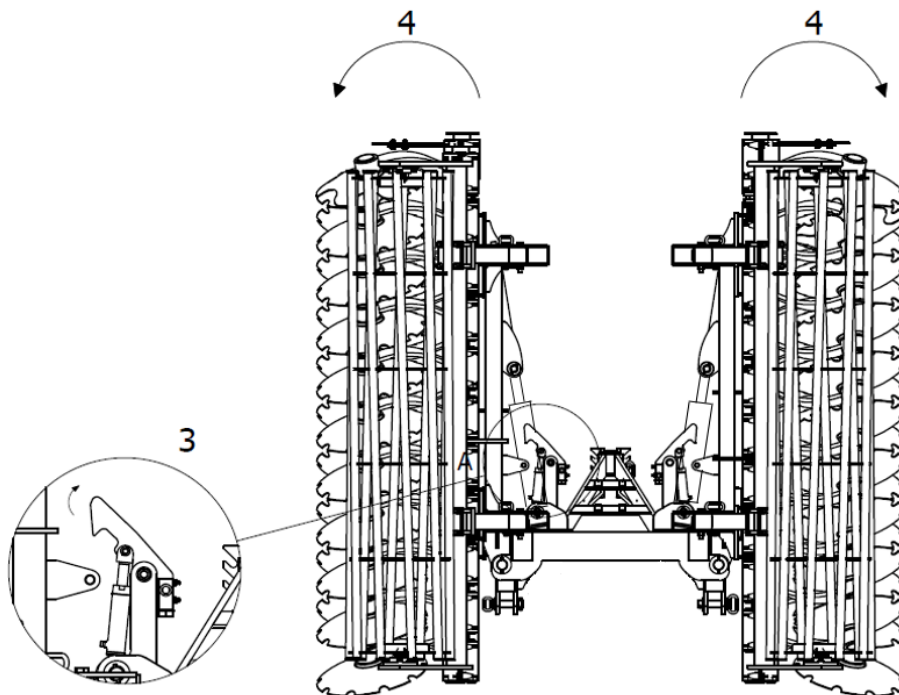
Séquence d'ouverture de la machine (3 - déverrouillage du crochet du système de blocage hydraulique des ailes; 4 - ouverture des ailes de la machine)
